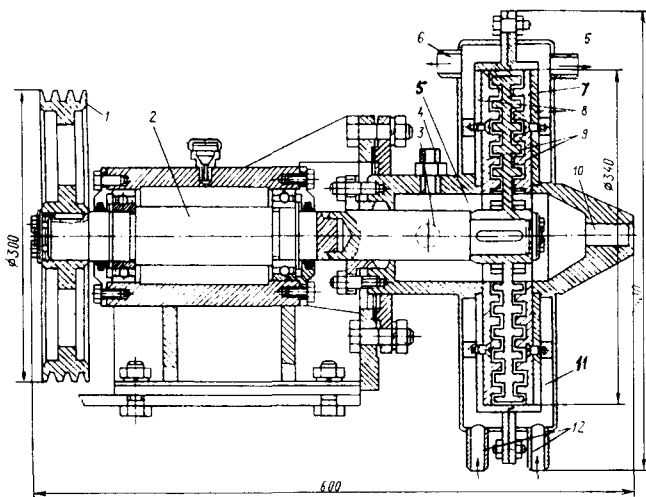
Роторный центробежный смеситель-эмульсатор
